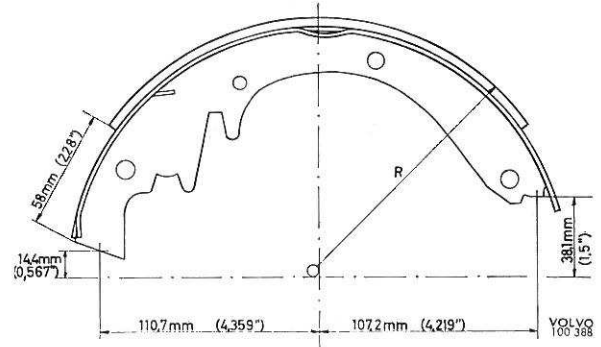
Cote de réglage pour segments arrière des roues avant.
